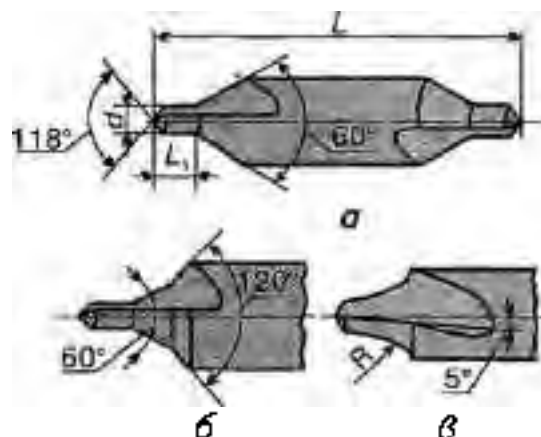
ЦЕНТРУВАЛЬНІ СВЕРДЛА
